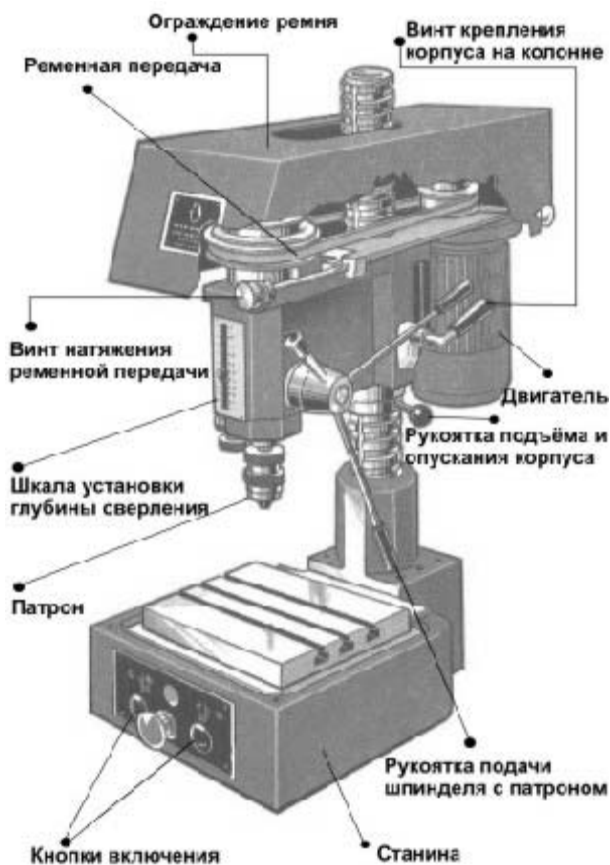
Вертикально-сверлильный станок 2М112
